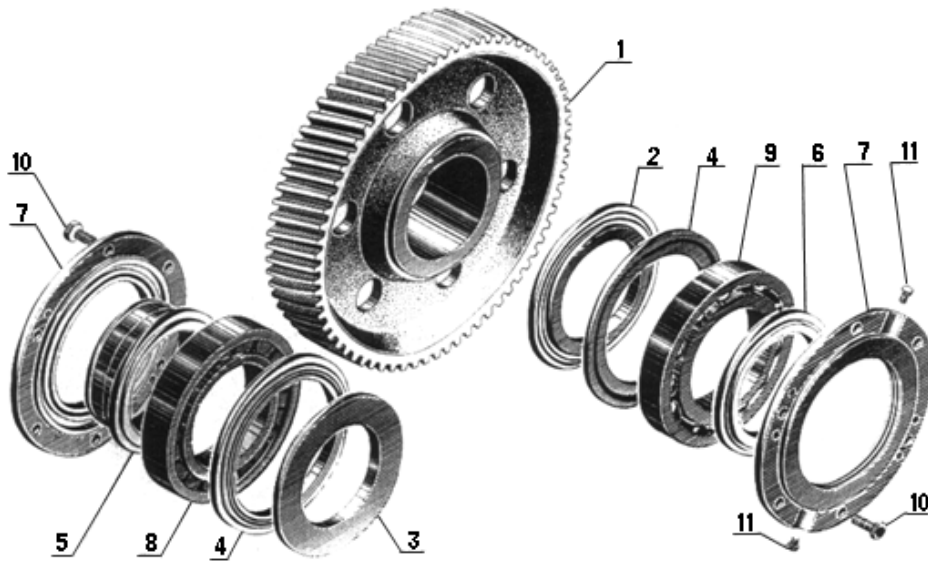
Колесо зубчасте тягового редуктора:
